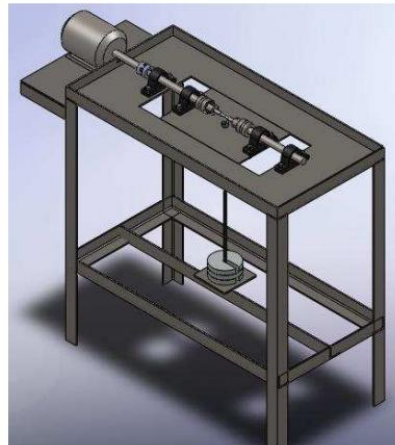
ESQUEMA DE MÁQUINA DE ENSAYOS MOORE
